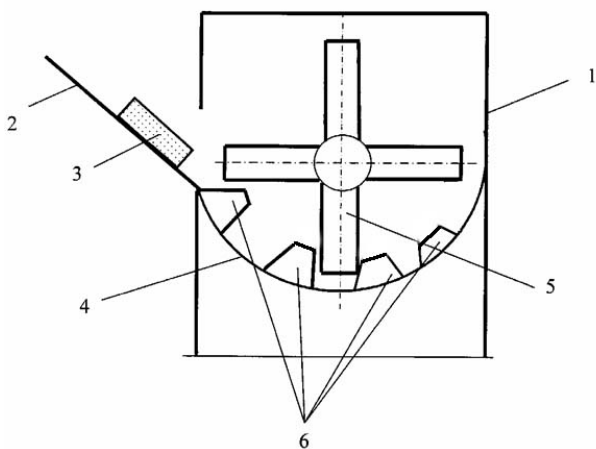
Варіант одновалкової зубчастої дробарки із звичайним ротором
